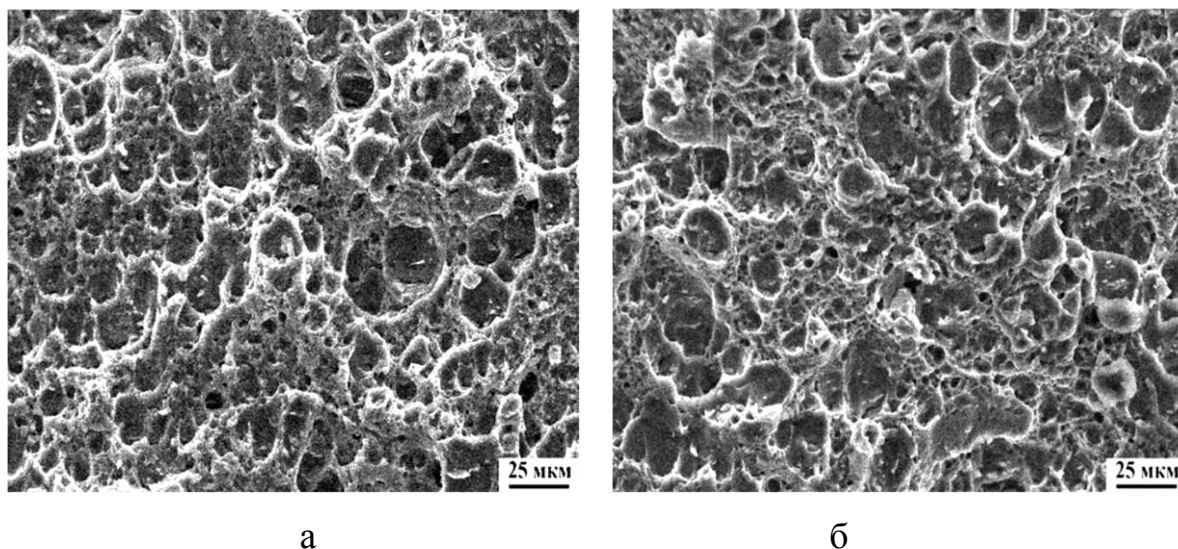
Микроструктура поверхности разрушения образцов ядра сварного шва сплава системы Al–Cu–Mg: а – вдоль направления сварки; б – поперек направления сварки
